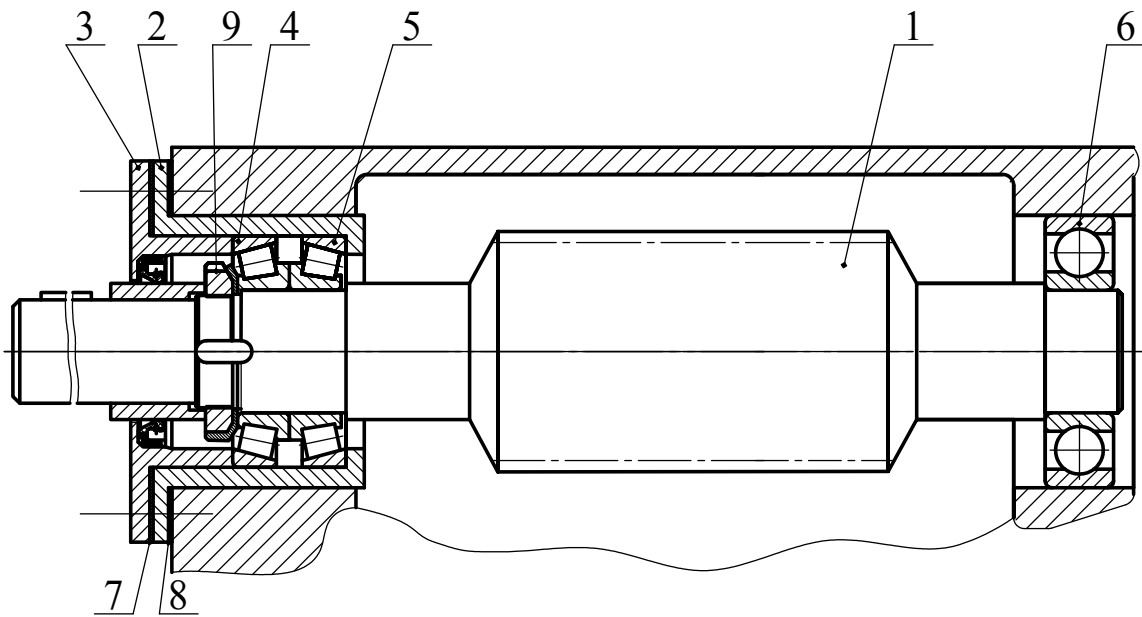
Конструкція підшипникового вузла черв'яка
